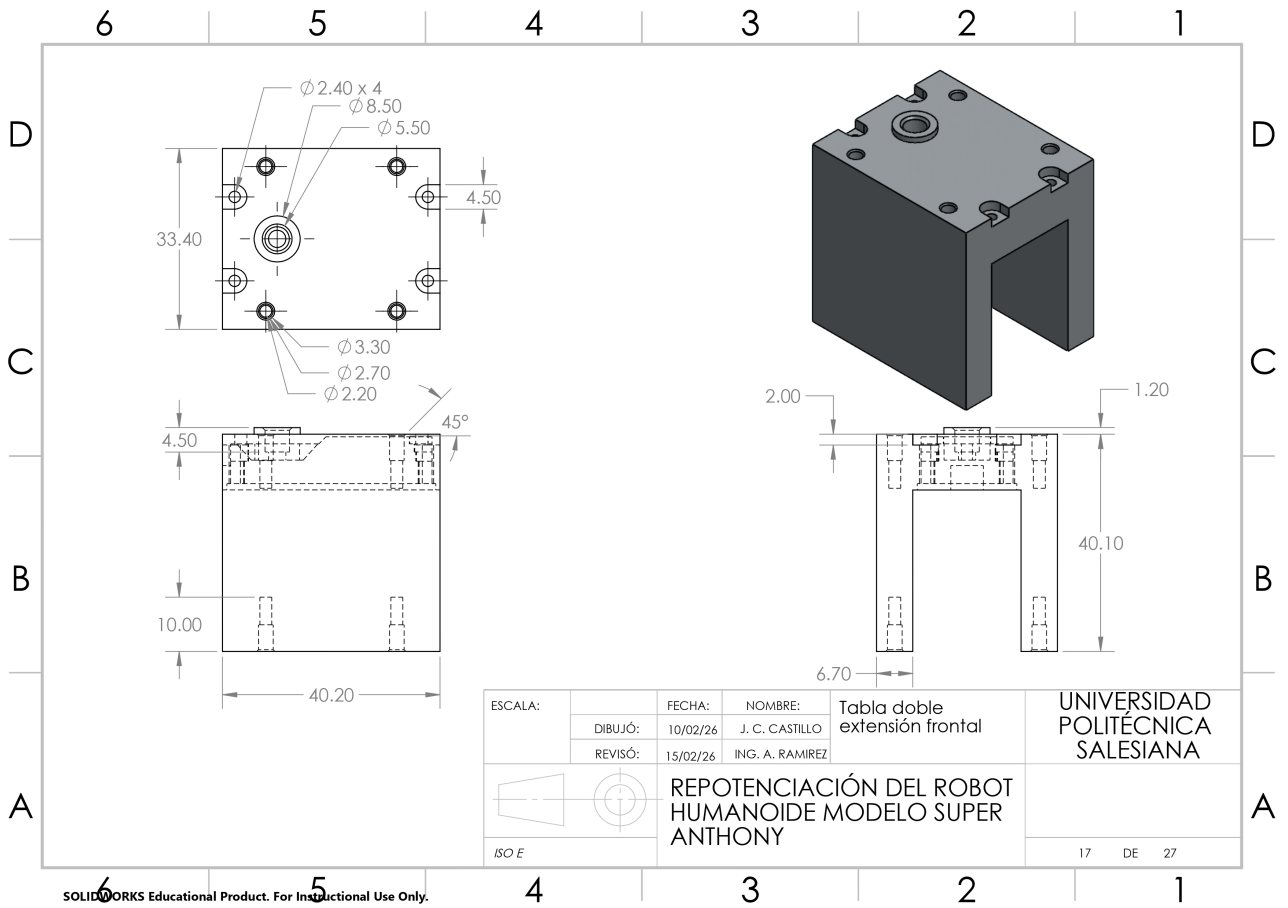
Lámina acotada de la tapa con doble extensión frontal del robot humanoide, por J. Castillo y B. Gualle, Solidworks
